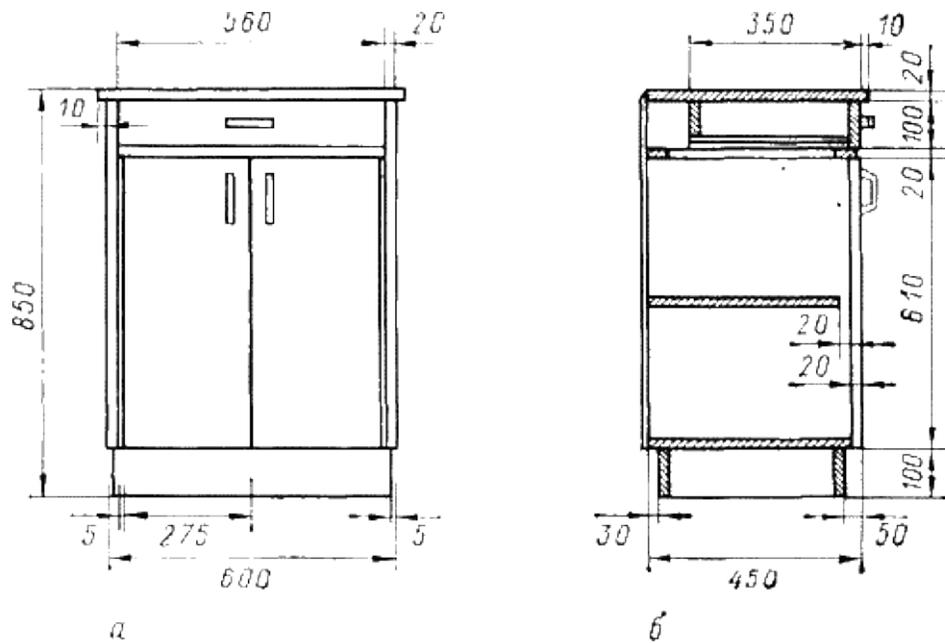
Эскиз разделочного стола-шкафа: а — вид спереди; б — поперечный разрез
